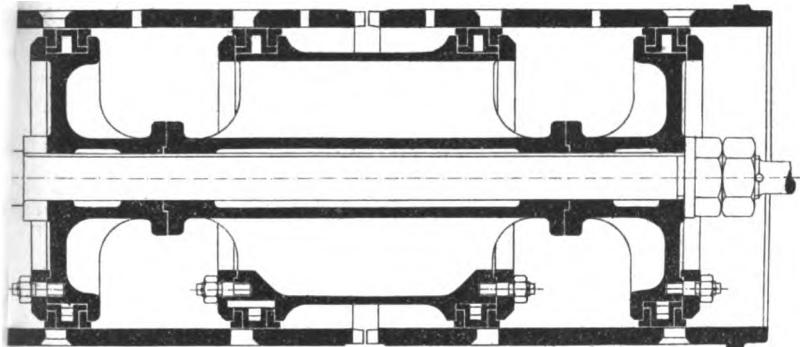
Kolbenschieber. Maßstab 1:9,42.
